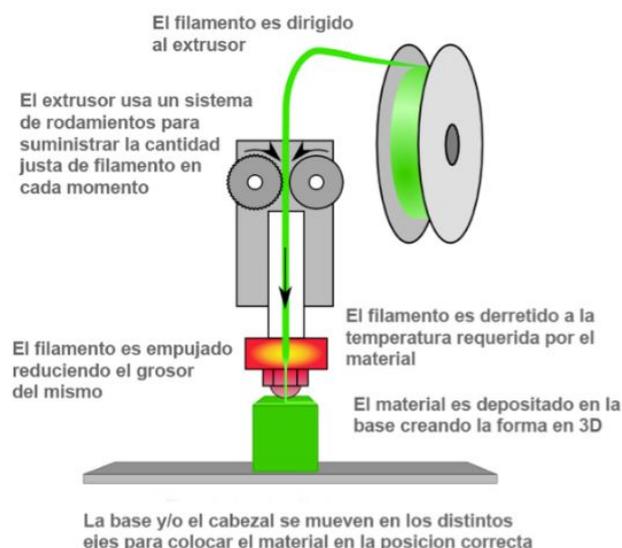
Técnica FDM (Fuente: www.taringa.net)
